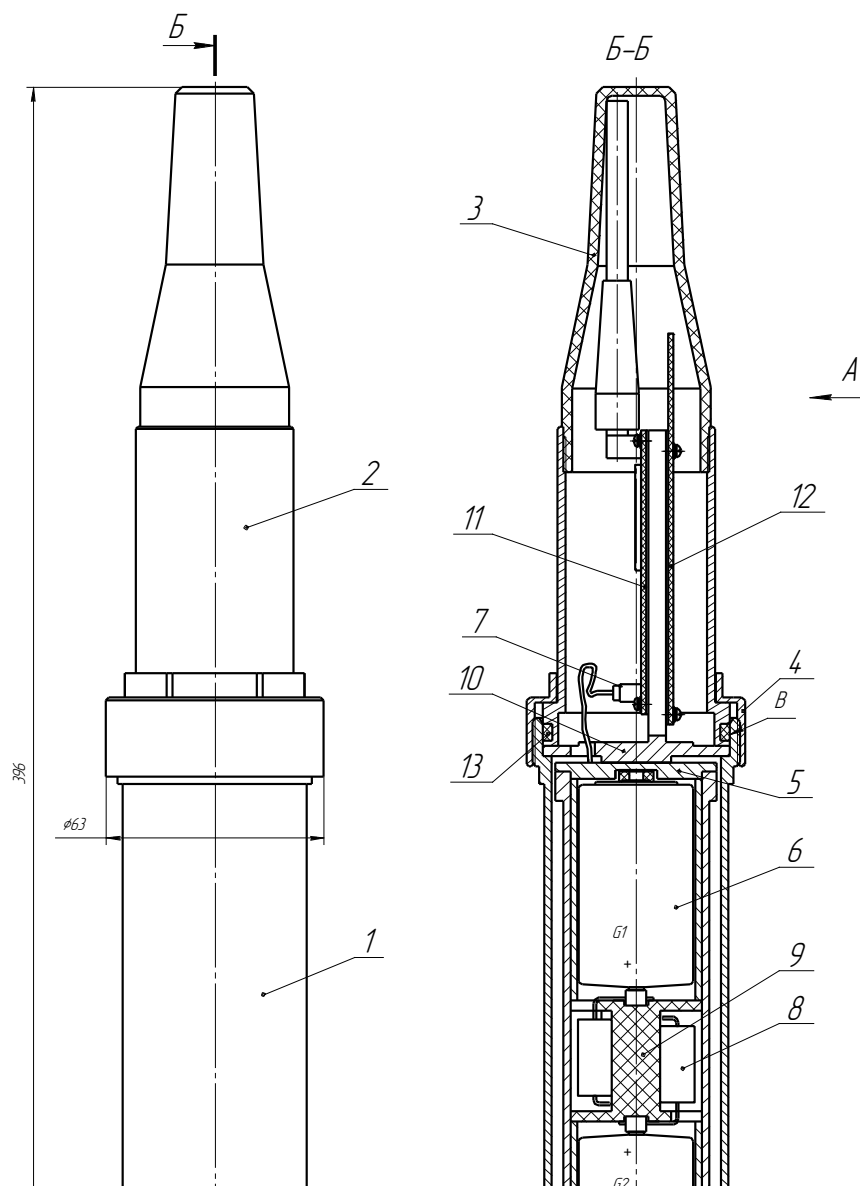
Внешний вид, состав, габаритные и присоединительные размеры МСiС
